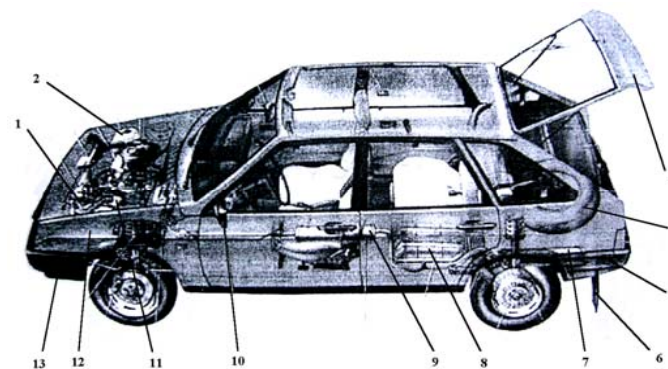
Устройство автомобиля ВАЗ 2109: 1 – АКБ, 2 – бачок омывателя ветрового стекла, фар, 3 – дверь задка, 4 – запасное колесо, 5 – бампер задний, 6 – фартук заднего крыла, 7 – глушитель основной, 8 – бак топливный, 9 – глушитель дополнительный, 10 – зеркало заднего вида наружное, 11 – бачок расширительный, 12 – крыло переднее правое, 13 – бампер передний.
